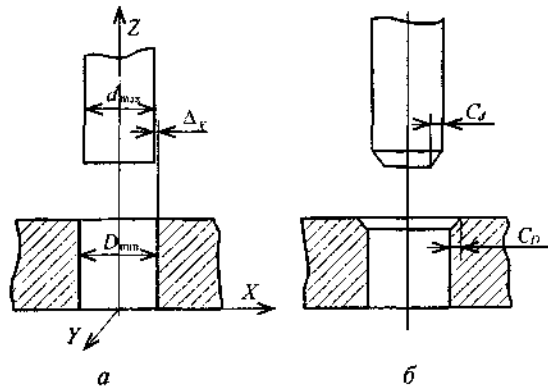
Схема сборки деталей, сопрягаемых по цилиндрическим поверхностям: а — детали без фасок; б — детали с фасками
